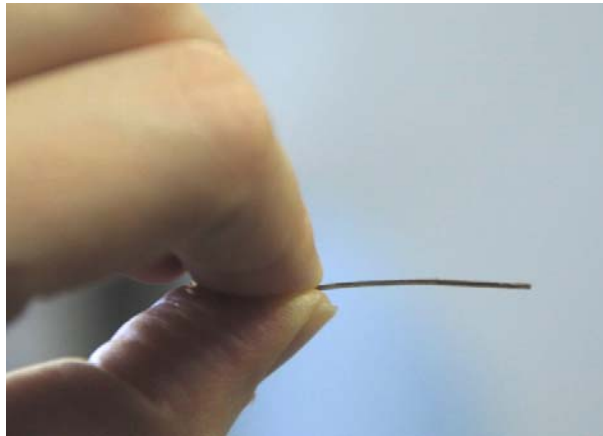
Corte de couro a laser, com largura de 0,5 mm
